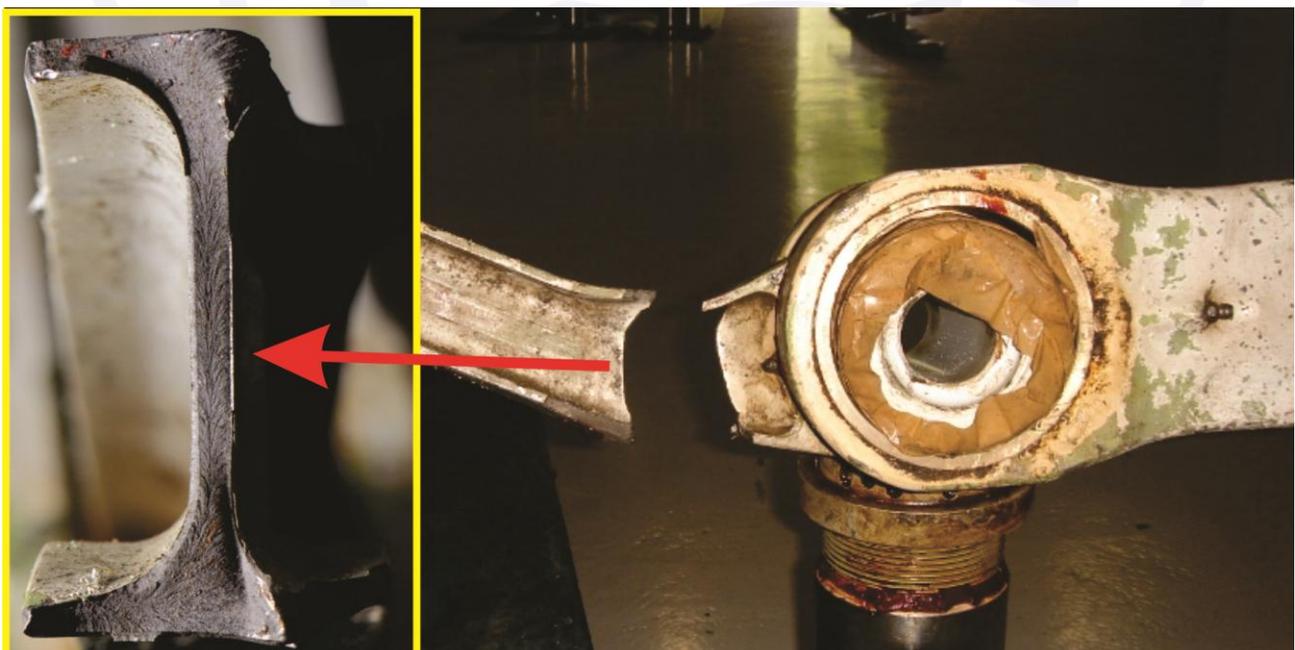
Braço articulado fraturado visto de lado e de frente. Fratura por sobrecarga.
